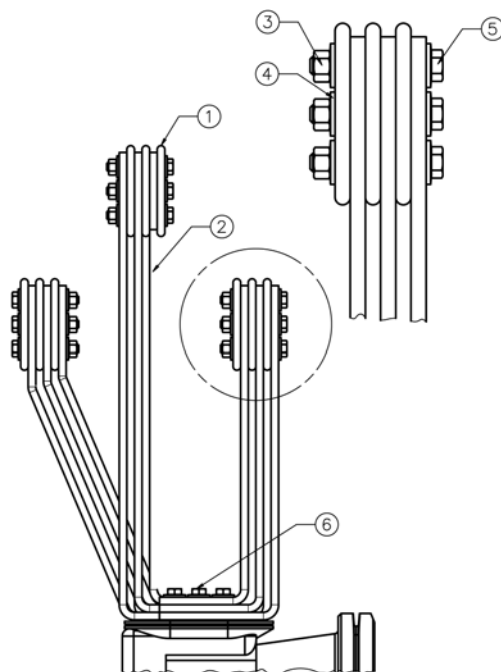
Боковой вид шинной конструкции 3150/4000 А, панели фидера 3150/4000 А (кожухи шинной изоляции сняты)
